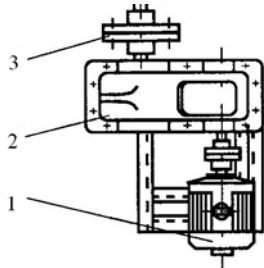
Схема привода пластинчастого конвеєра: 1 – електричний двигун; 2 – редуктор; 3 – муфта
